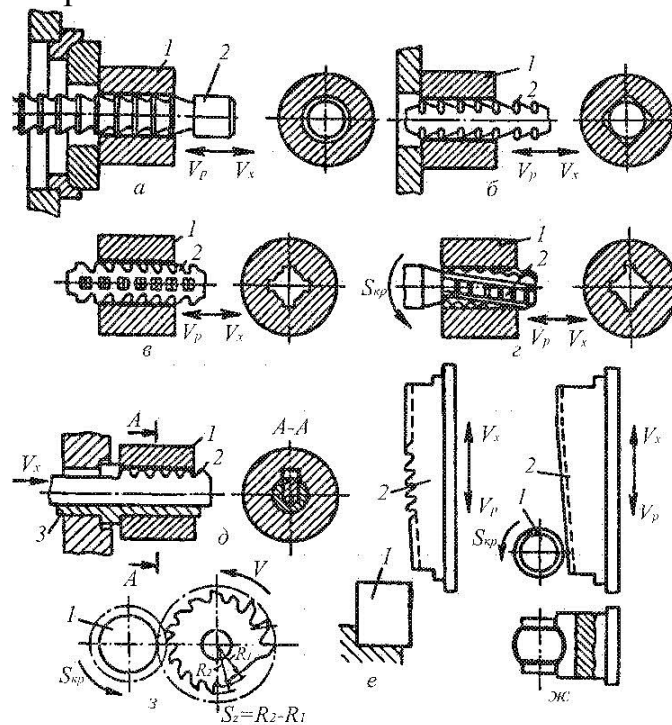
Схеми обробки поверхнь заготовок на протяжних верстатах
